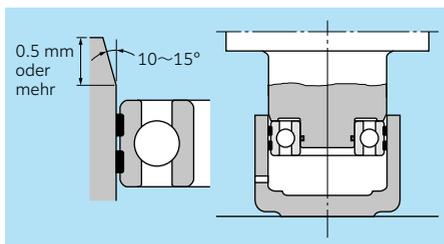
Montagemethode und Einführschräge am Gehäuseinnendurchmessers
